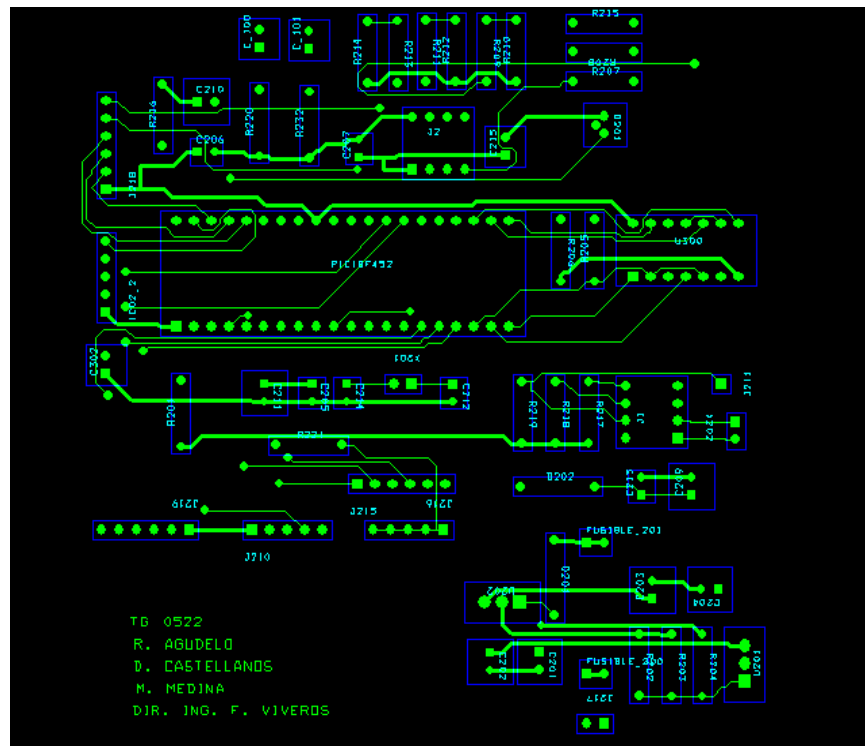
Diseño de tarjeta en Layout de OrCAD ®
